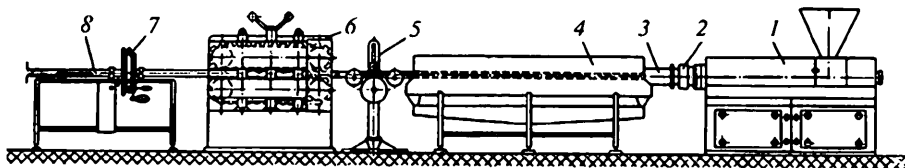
Схема экструзионного агрегата для изготовления труб
